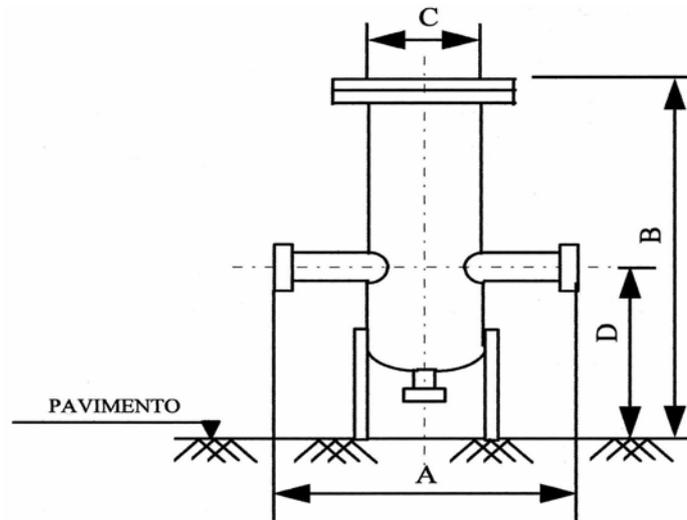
Esquema de dimensiones del filtro principal de la E.R.M.
